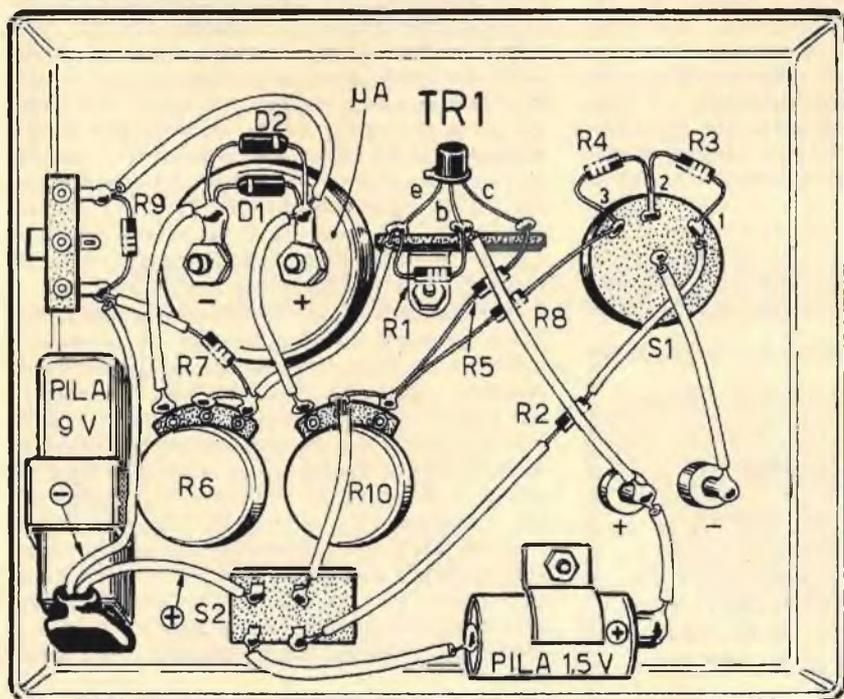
Cablaggio dell'ohmmetro elettronico nella parte interna del contenitore.
